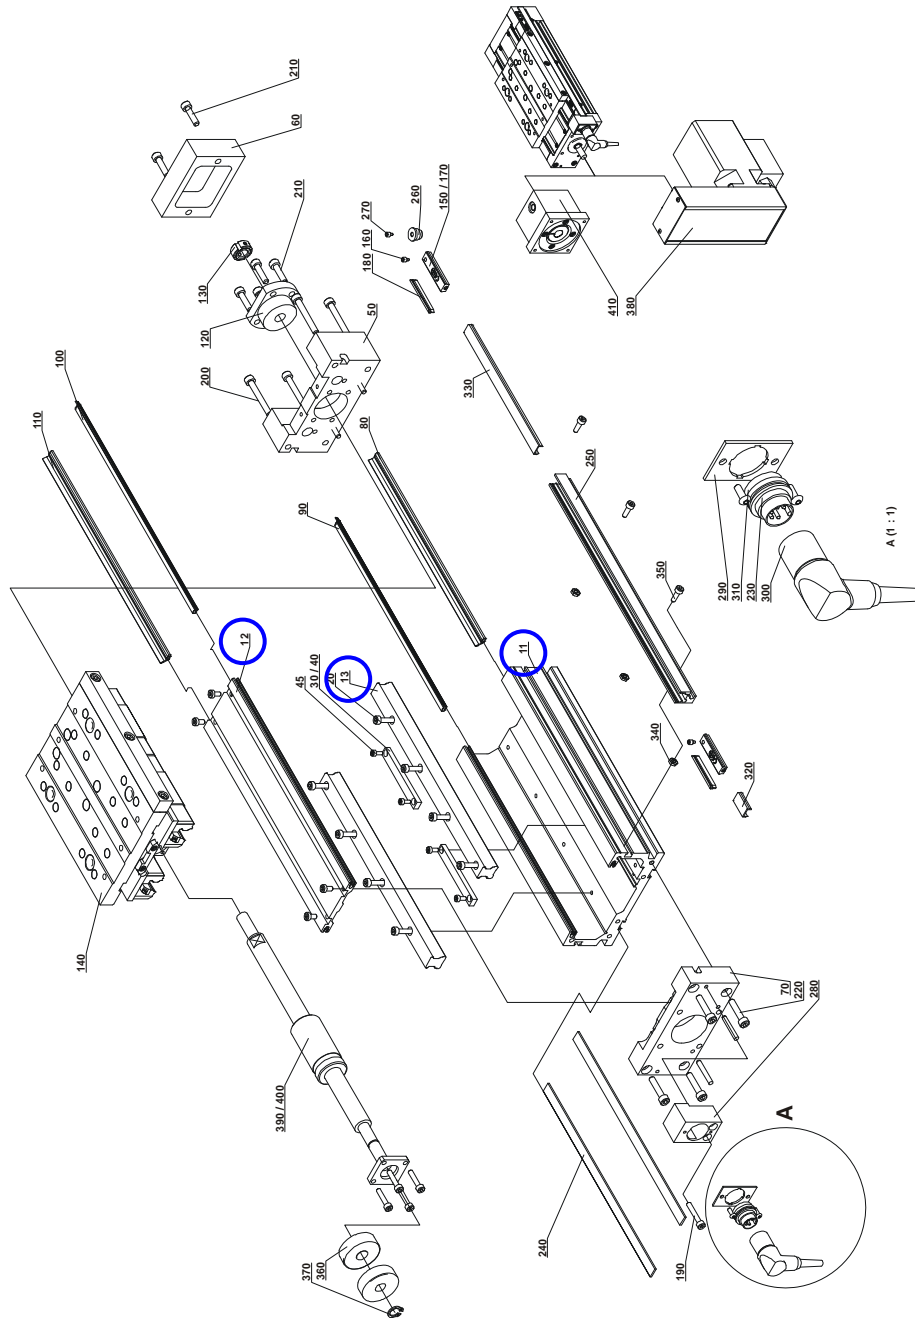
Teilegruppe TG1000604, Explosionszeichnung
